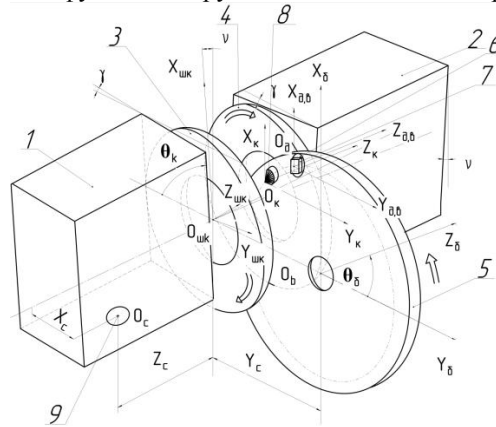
Розрахункова схема формоутворення торців циліндричних деталей з некруглим профілем
